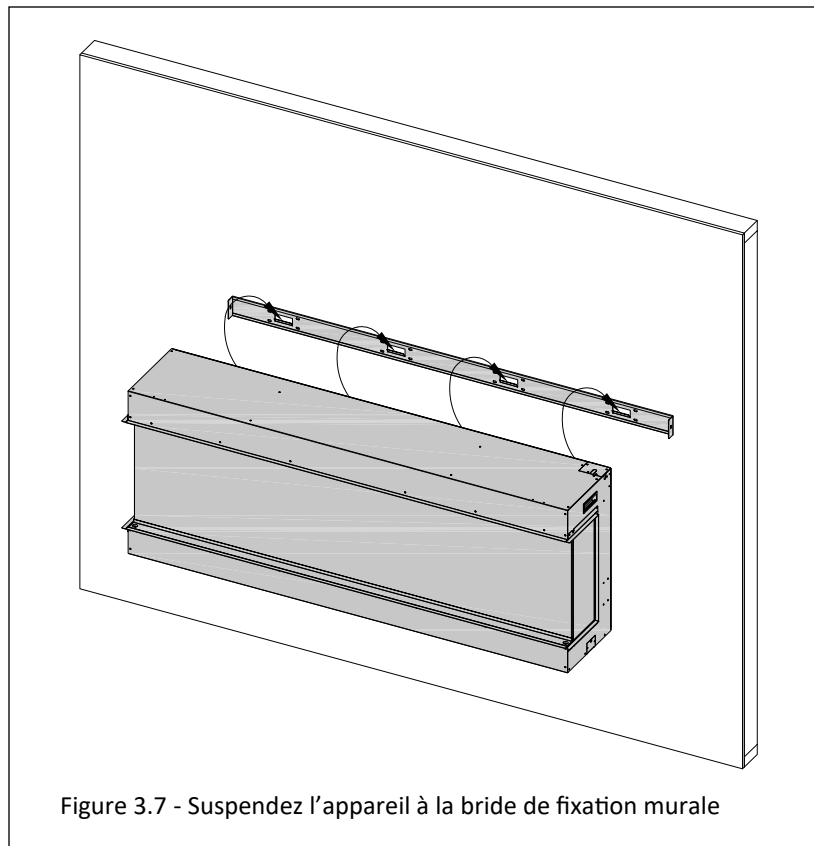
Suspendez l'appareil à la bride de fixation murale
